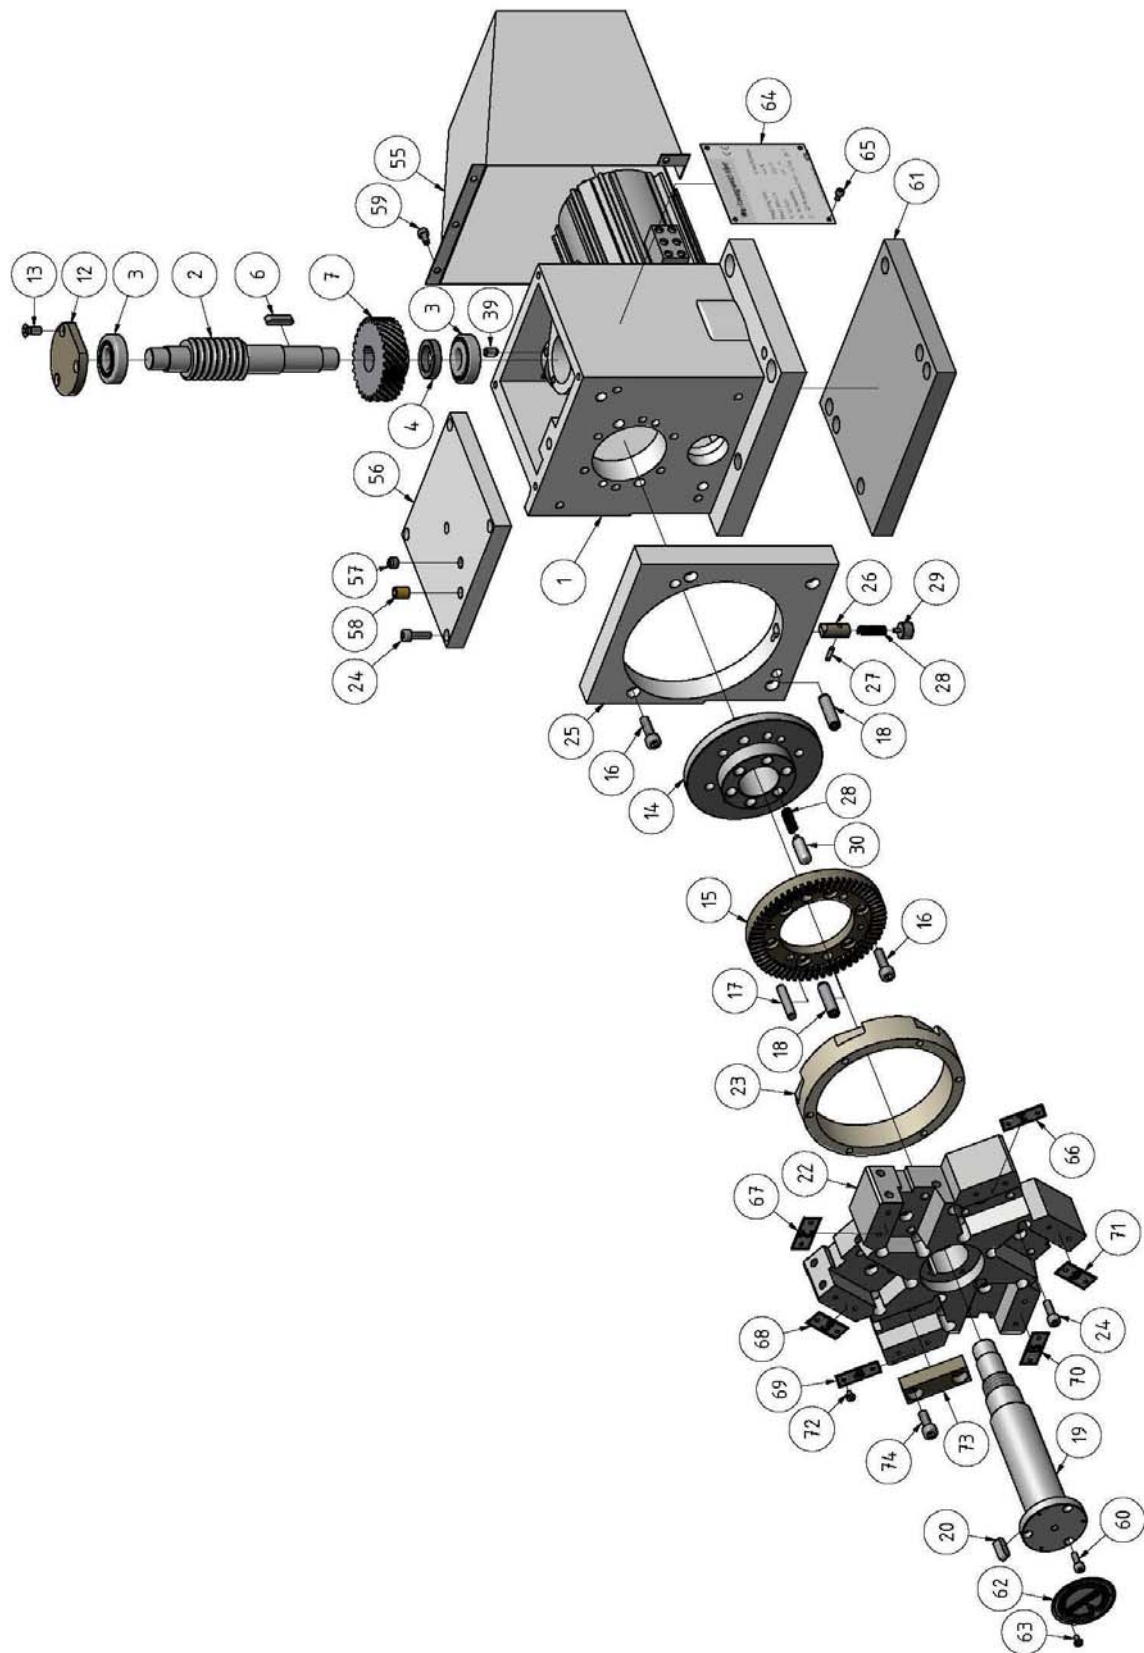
Werkzeugwechsler 2-2 - Tool changer 2-2
